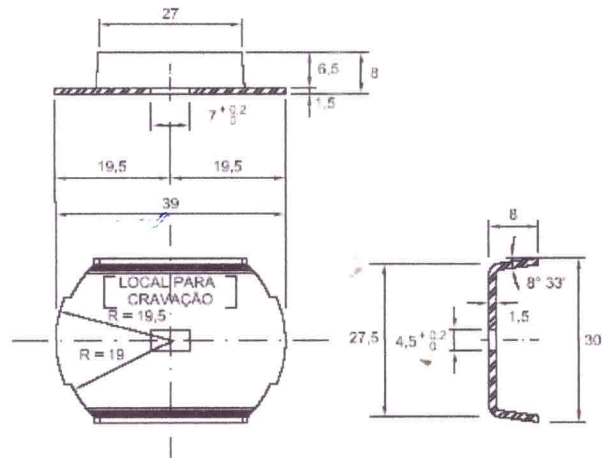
DETALHE DA ARRUELA DE FIXAÇÃO.
